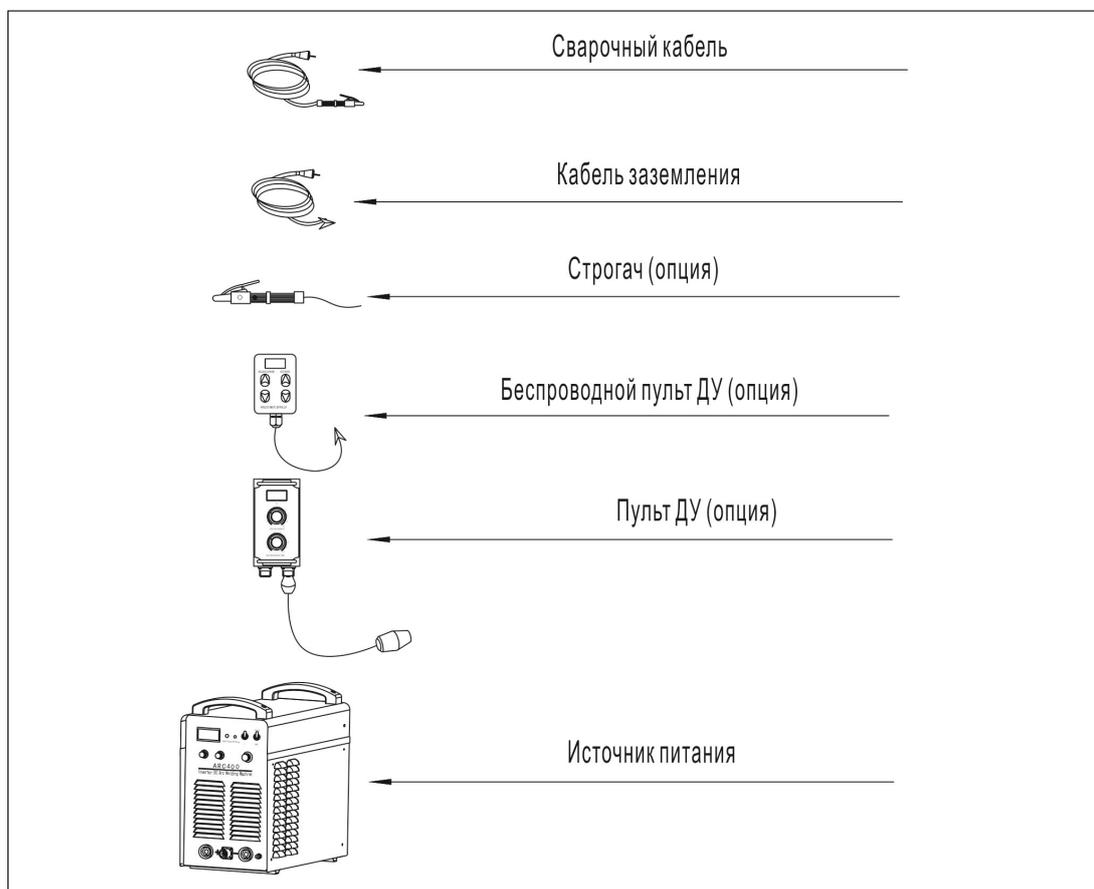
Основные элементы сварочной системы
